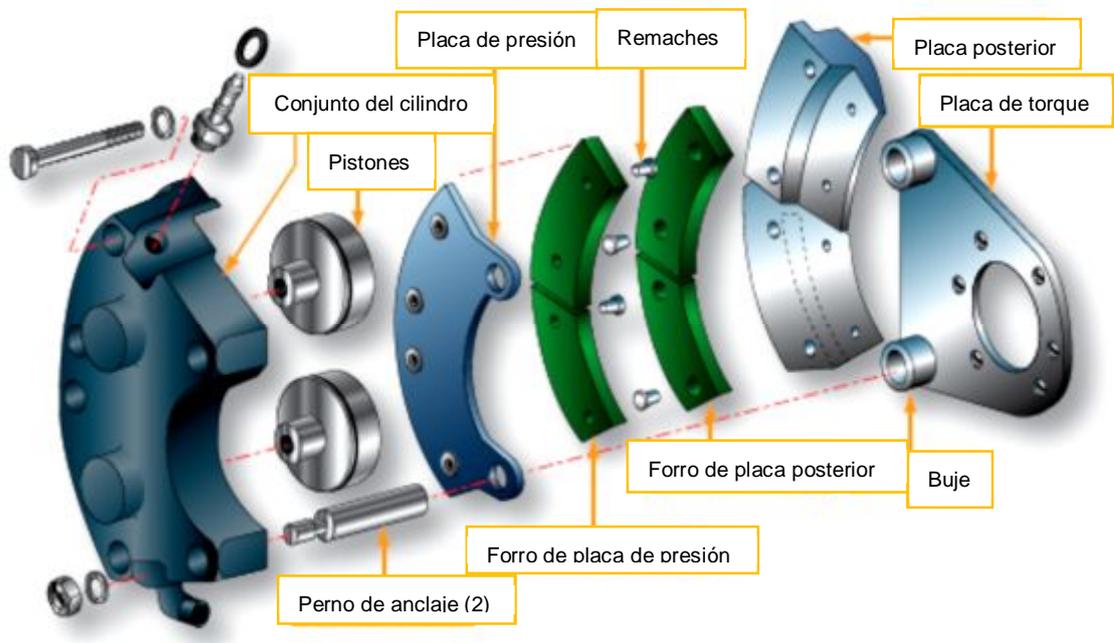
Vista en despiece de un freno Cleveland de doble pistón.
